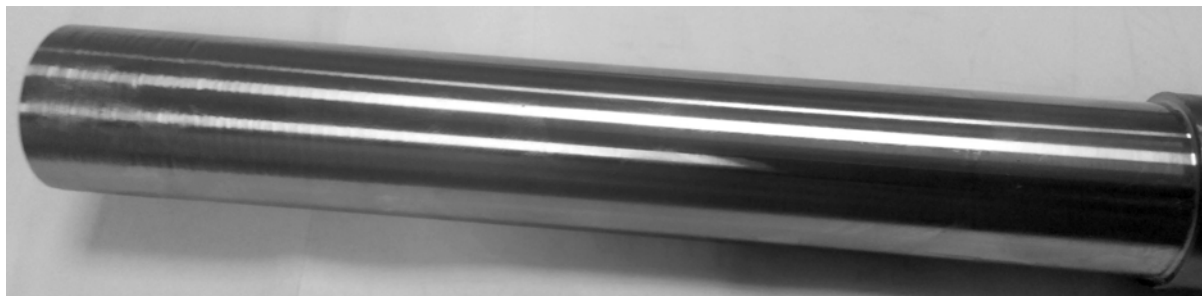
Результат обробки консольно закріпленої нежорсткої заготовки на режимах характерних для швидкісної обробки
